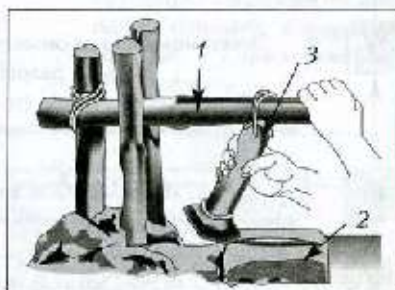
Древнее приспособление для резки камня: 1 — нажимной рычаг; 2 — заготовка; 3 — оправка (совершает качательное возвратно-поступательное движение)
